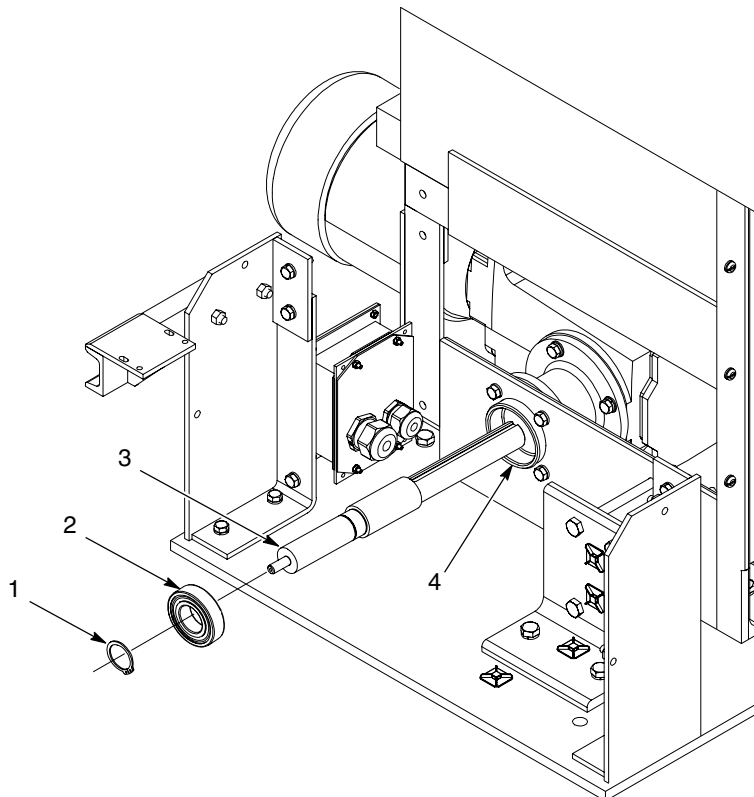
Sustitución del cojinete o del eje del motor de engranajes
